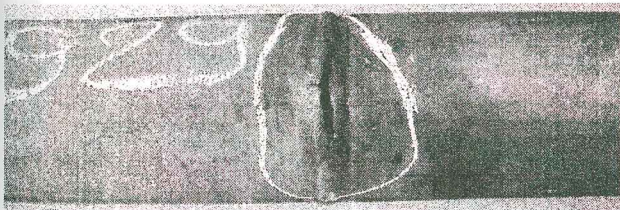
Фрагмент печной трубы с трещиной в сварном шве
